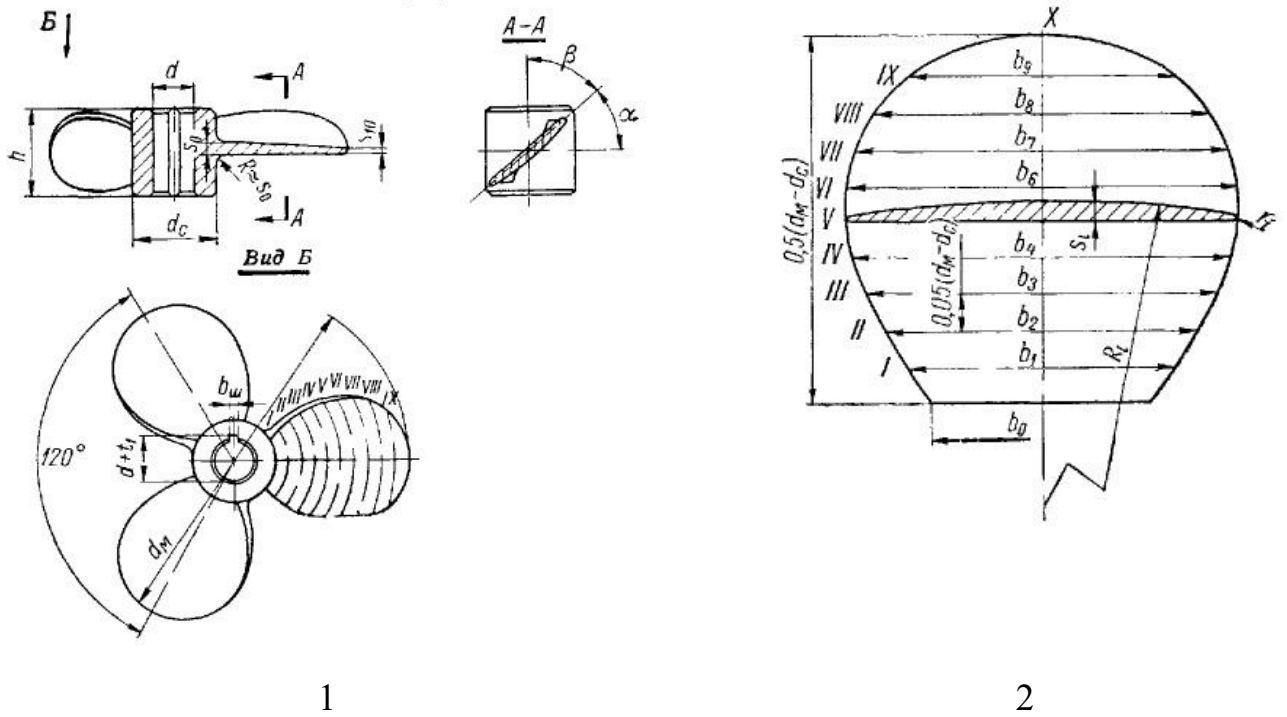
Трилопатевий пропелерний перемішувачий пристрій [13]: 1 – конструкційні особливості; 2 – розгортка лопаті
